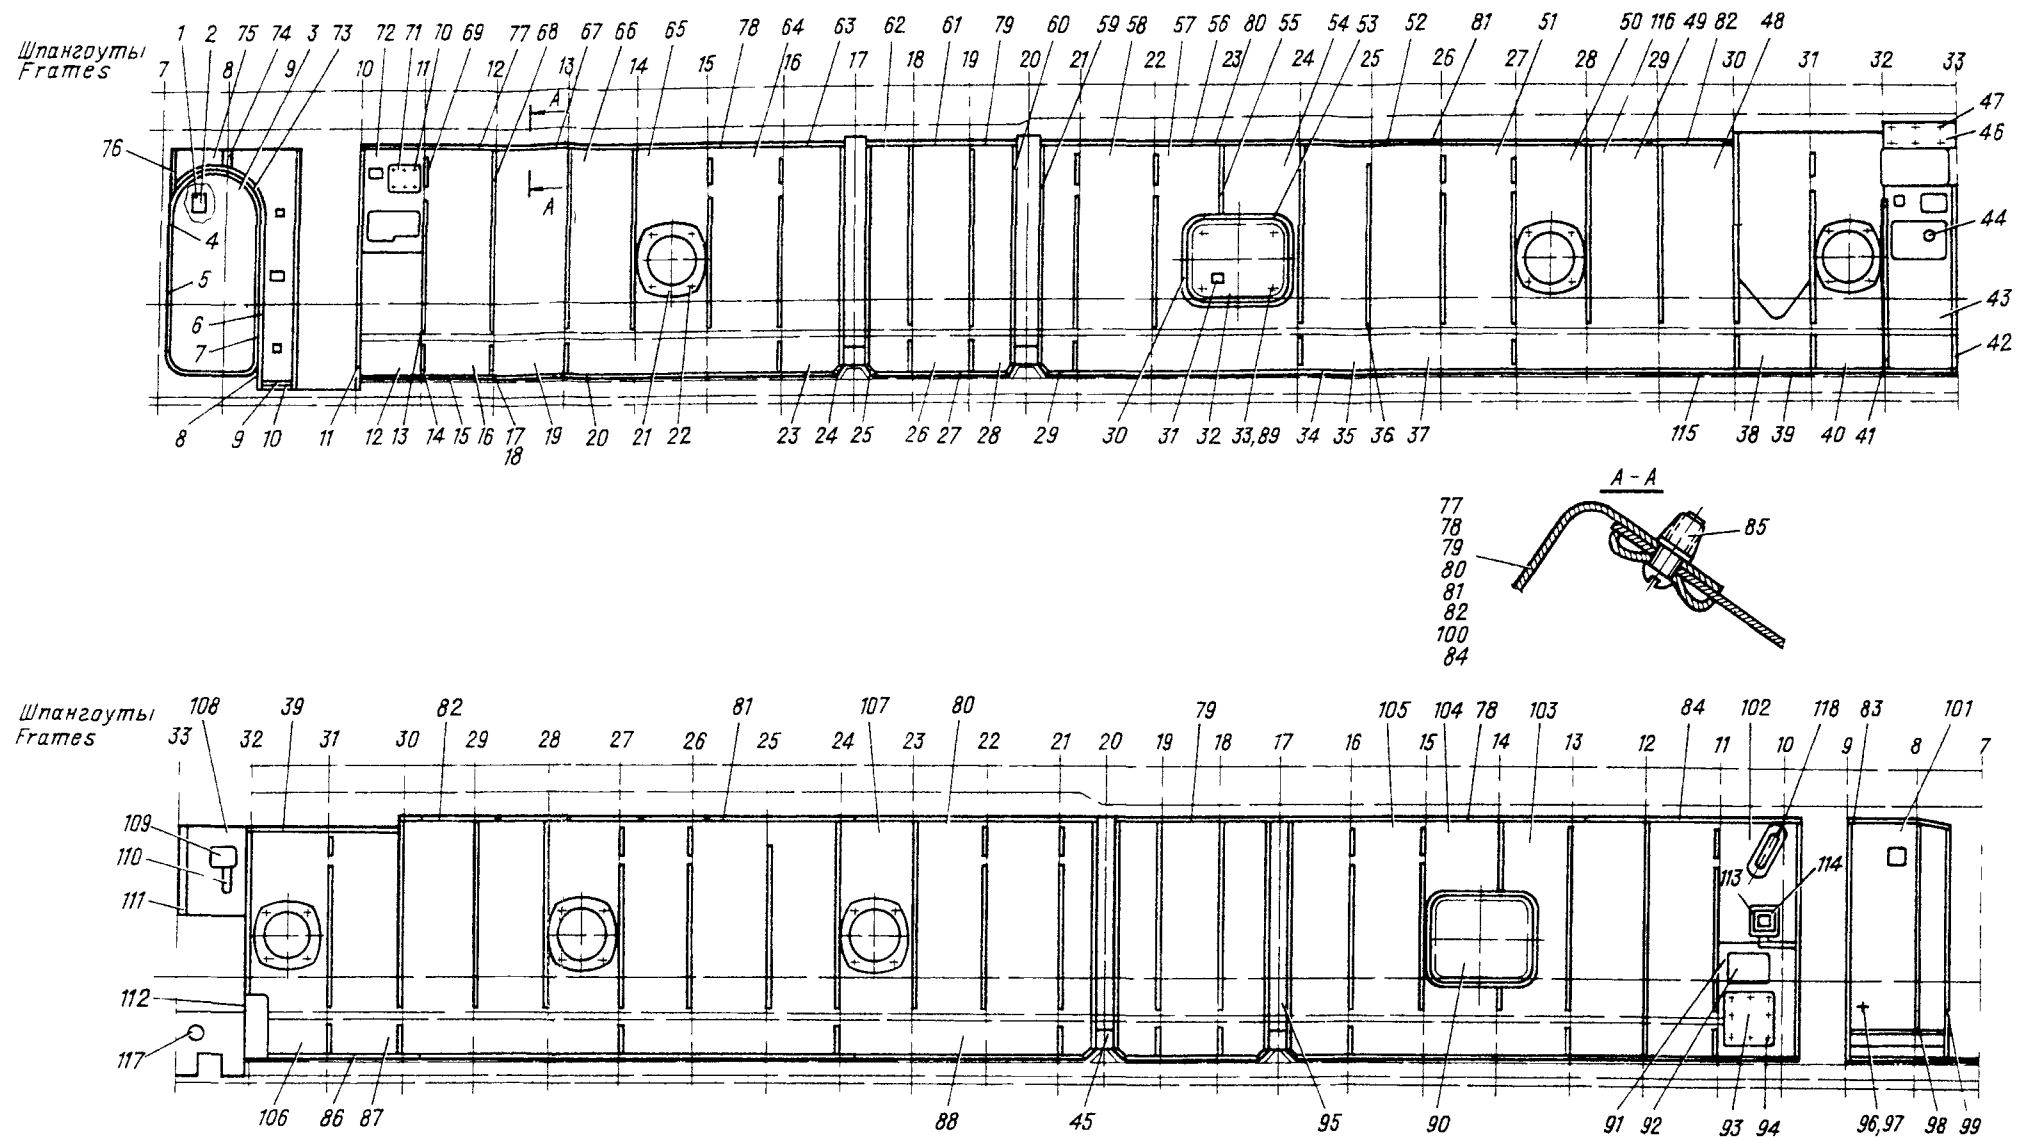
ОБЛИЦОВКА БОРТОВ МЕЖДУ ШПАНГОУТАМИ 7-33
